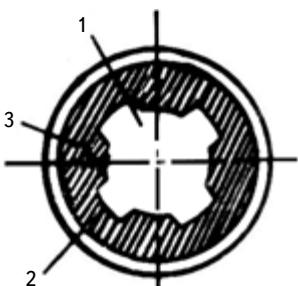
Калибр ствола нарезного ручного огнестрельного оружия:
